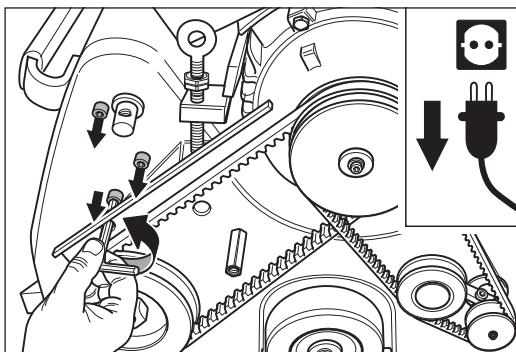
Lösen und entfernen der drei Befestigungsschrauben des Aggregates.
